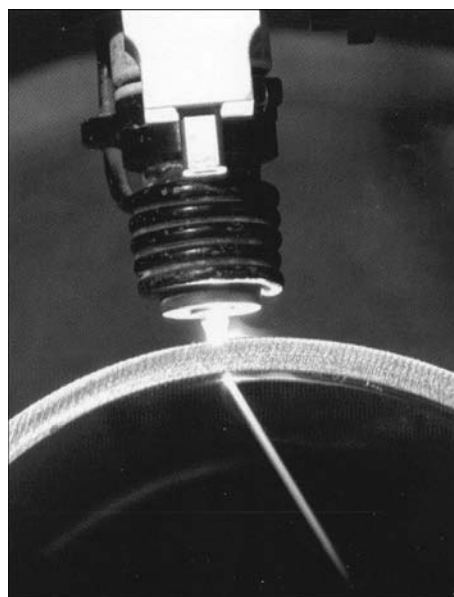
К-ТИГ сварка поворотного стыка трубы толщиной 13 мм
